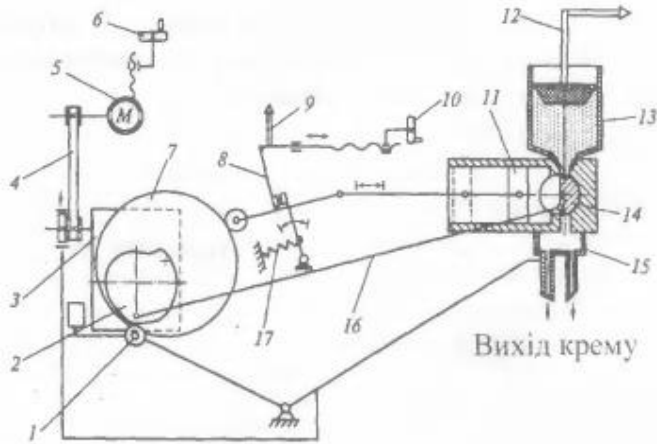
Кінематична схема дозатора крему: 1 – палець кривошипа; 2, 7 – кулачки; 3 – черв'ячний редуктор; 4 – клинопасова передача; 5 – електродвигун; 6 – рукоятка натягу паса; 8 – упор, що регулюється; 9 – стрілка-показчик дози крему; 10 – рукоятка для регулювання положення упору; 11 – поршень; 12 – поплавок з показчиком рівня крему; 13 – дозуючий пристрій; 14 – кран; 15 – насадки; 16 – тяга; 17 – пружини
